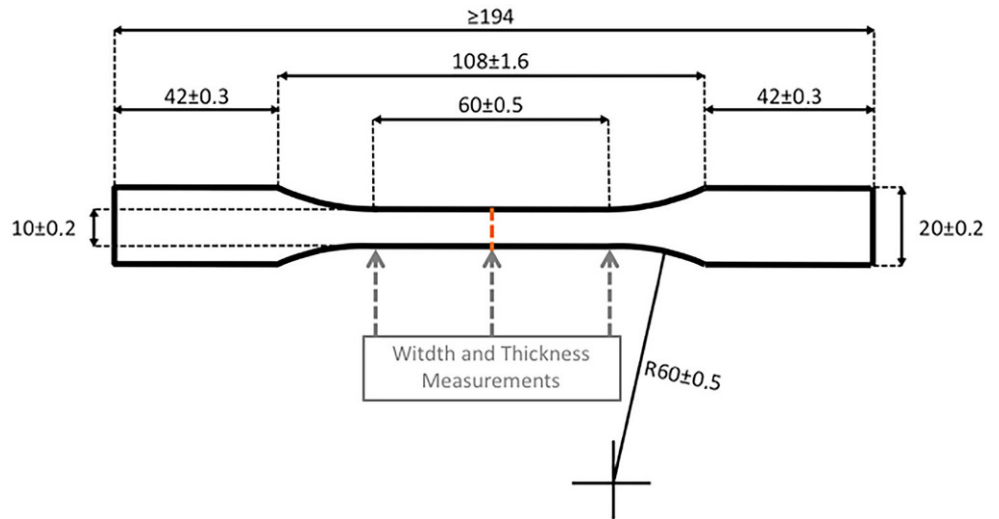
Schema modifizierter Probekörper Typ A2 mit Positionen der Dimensionsmessungen (Abmessungen in mm)
